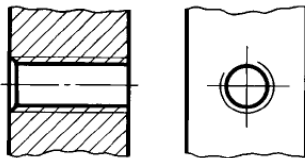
Изображение внутренней цилиндрической резьбы
